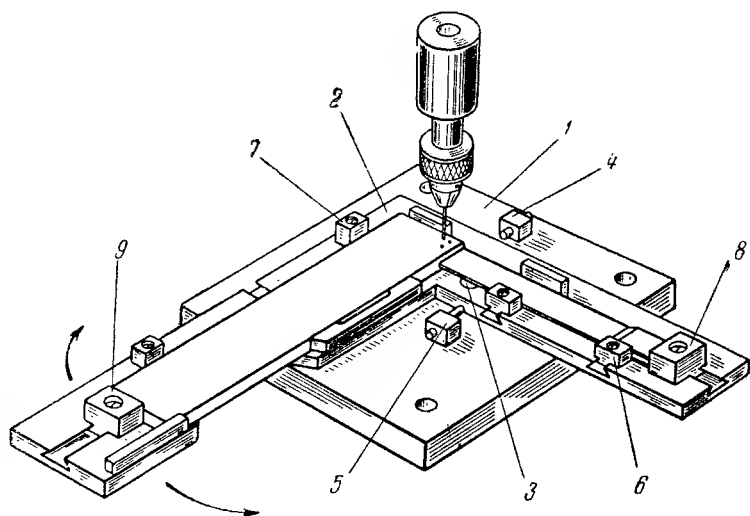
Универсальное качающееся приспособление для сверления отверстий под заклепки в пластине и в петушке
